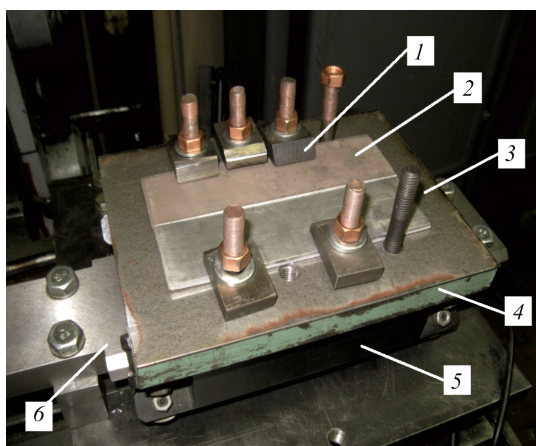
Приспособление для измерения продольных усилий при сварке:
